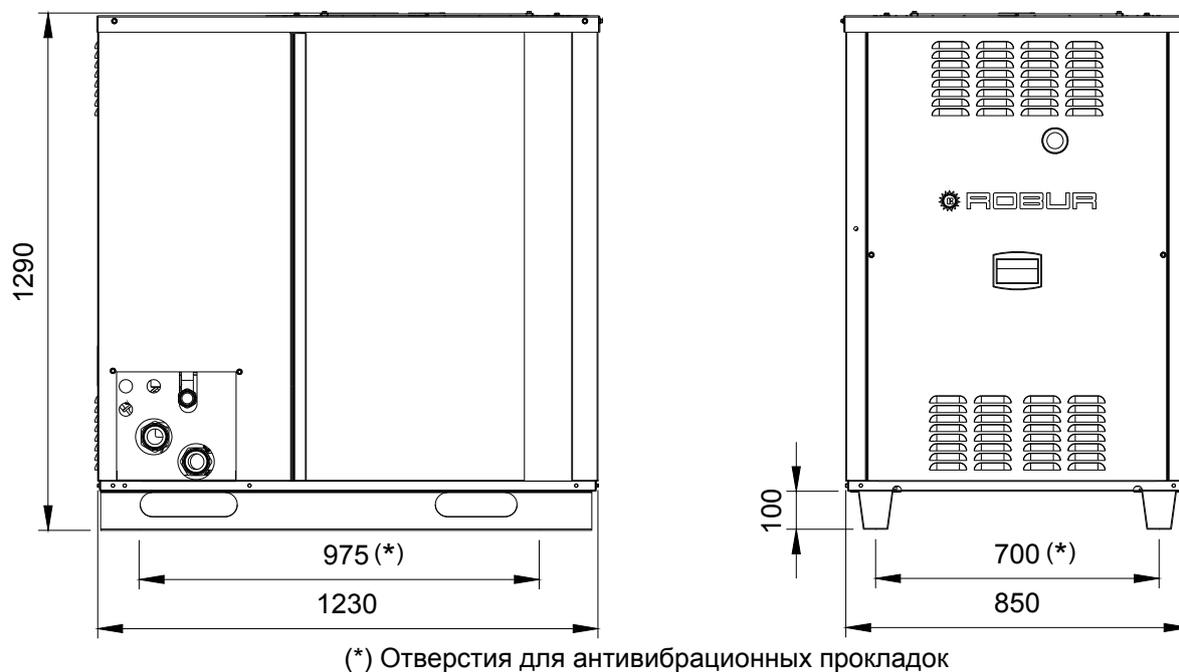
Габариты аппаратов "ACF60-00". Размеры пластины для соединений смотри на Рисунок 9, стр. 29
